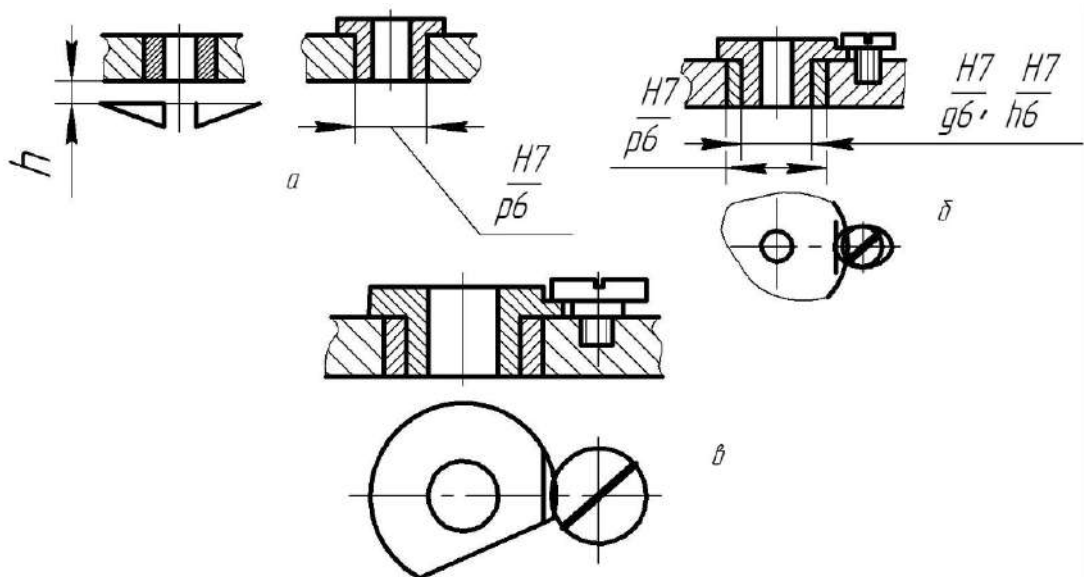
Конструкції втулок для спрямування інструменту
